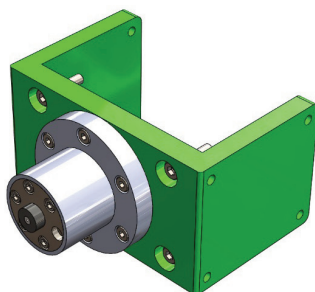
Трёхмерная модель корпуса штекерного разъёма пристыкованного к основной несущей лазерный диод детали (на рисунке обозначена зелёным цветом)
